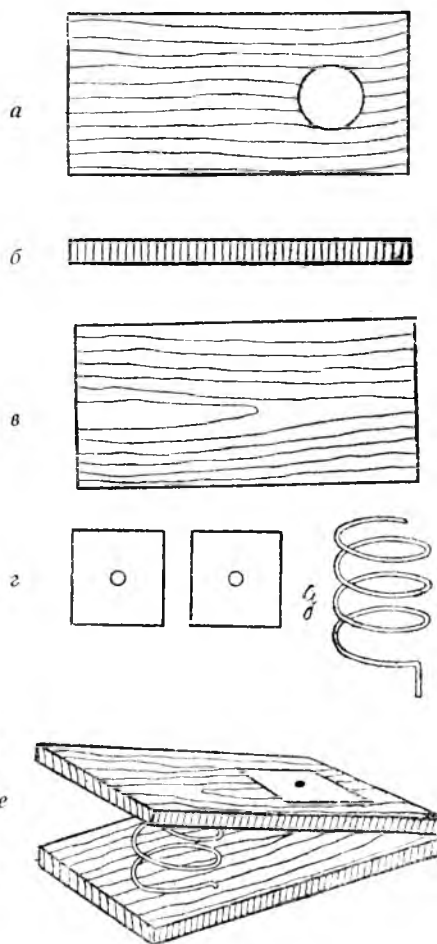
Детали и монтаж свистящего (флейтового) пищика:
